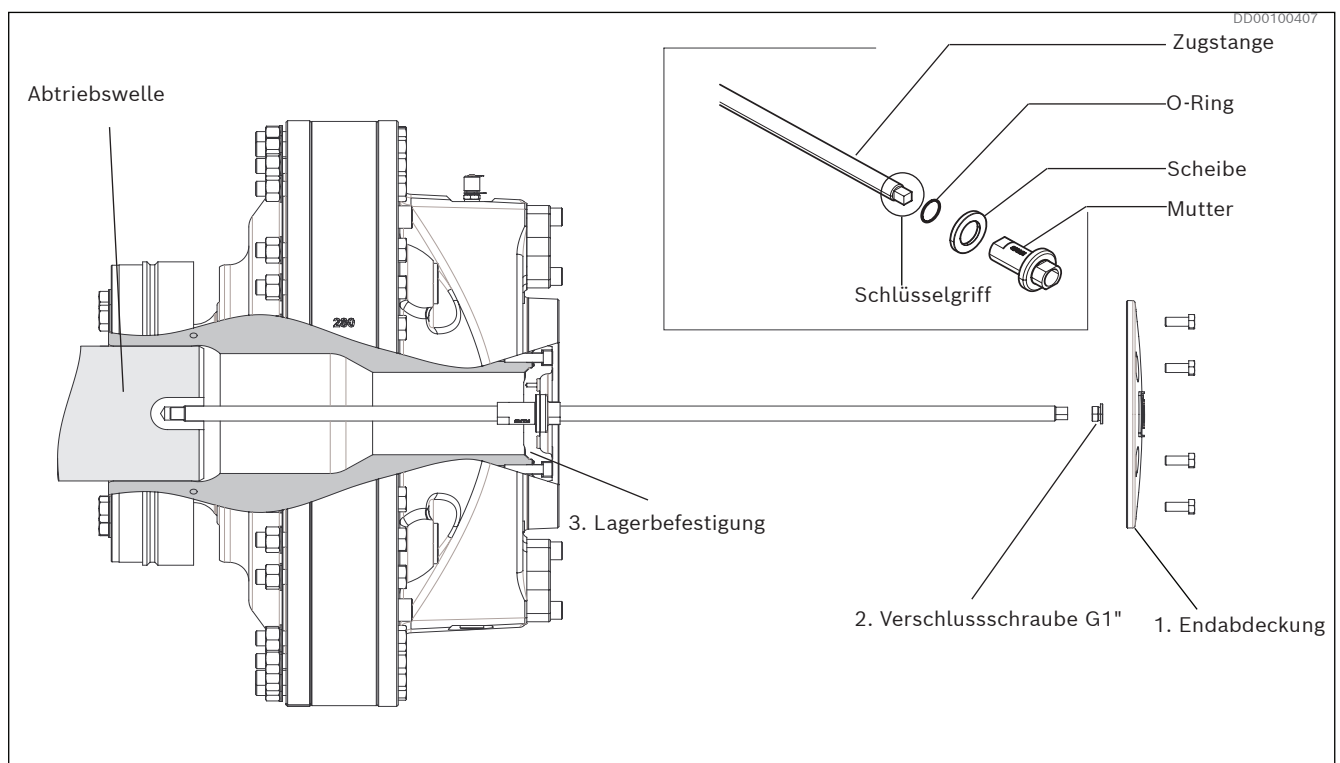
Montage von Kupplungsmotor mit Montagewerkzeug
